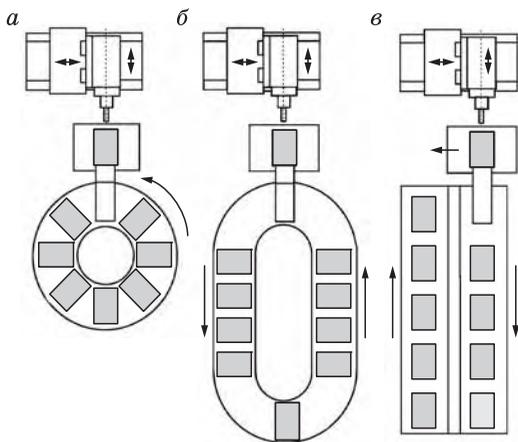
Подвижные магазины палет, используемые в ГПМ для обработки корпусов:
